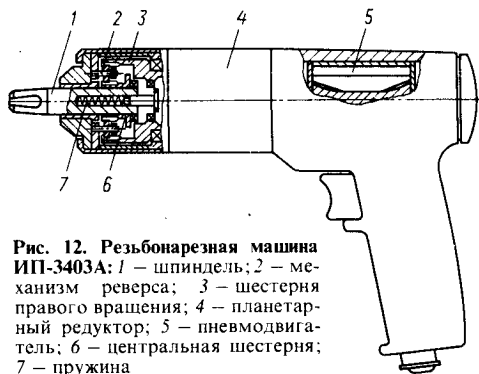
Резьбонарезная машина ИП-3403А: 1 — шпindel; 2 — механизм реверса; 3 — шестерня правого вращения; 4 — планетарный редуктор; 5 — пневмодвигатель; 6 — центральная шестерня; 7 — пружина
